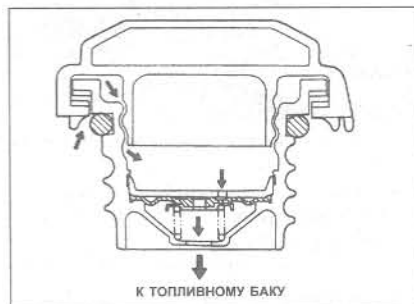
Разрез крышки заливной горловины топлива (Глава 11)
